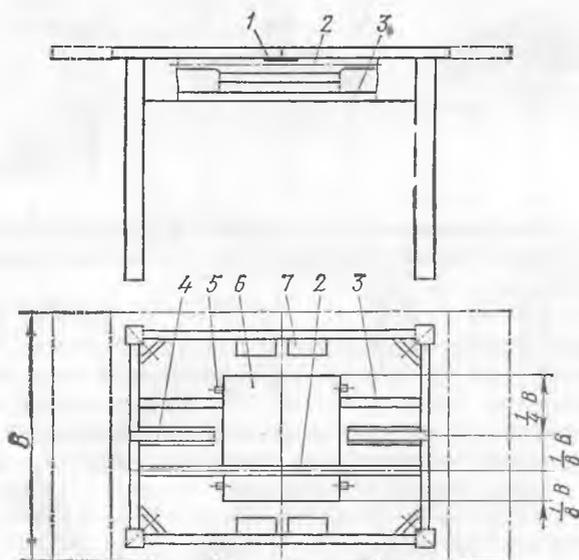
Конструкция стола с раздвижными крышками и неподвижным прямоугольным подстольем:
